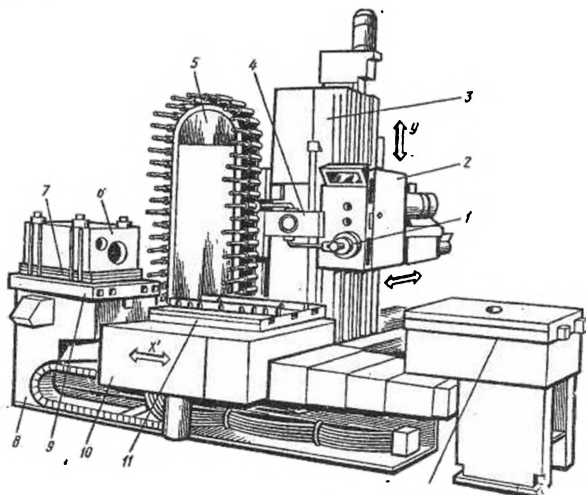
Горизонтальний багатоцільовий верстат
